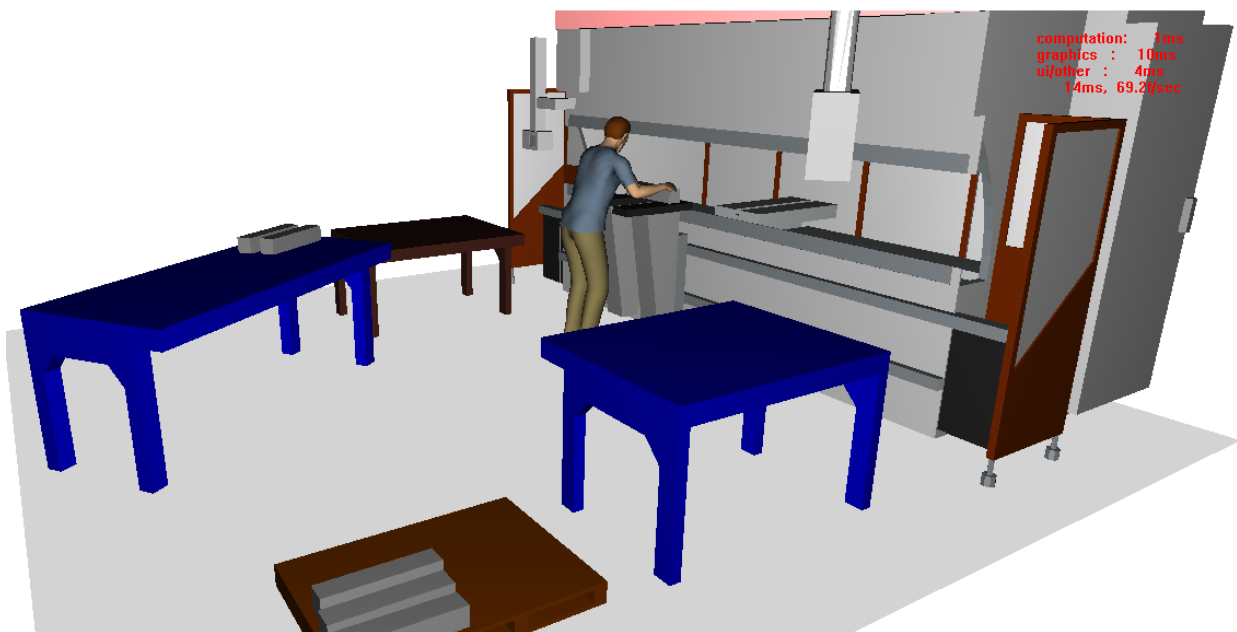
3D layout situace po nákupu nových technologií
